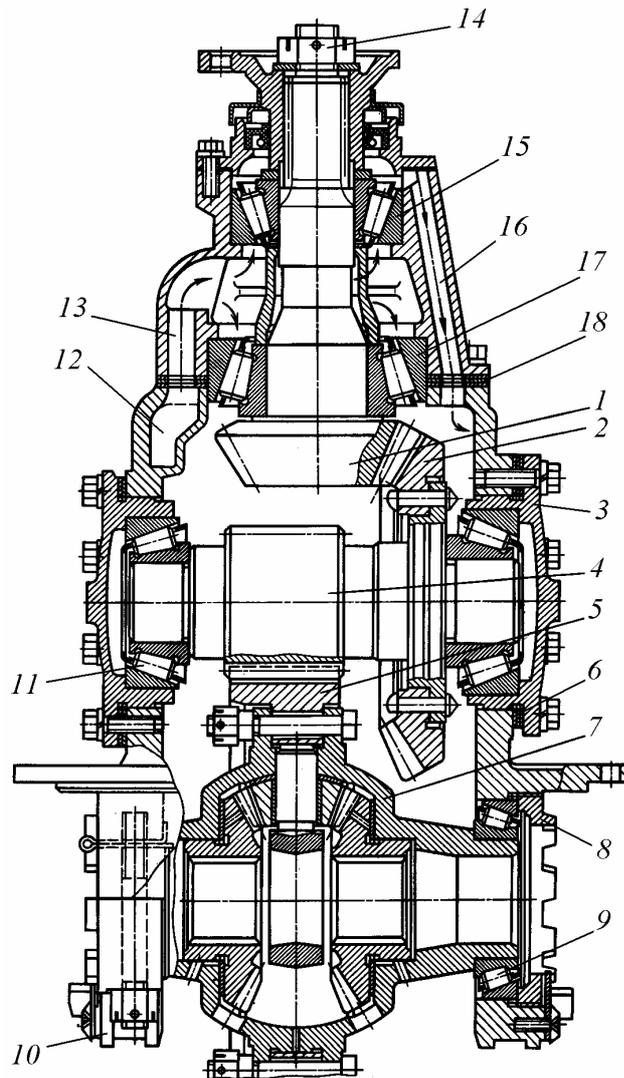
Двойная центральная передача с валами, расположенными в одной плоскости
